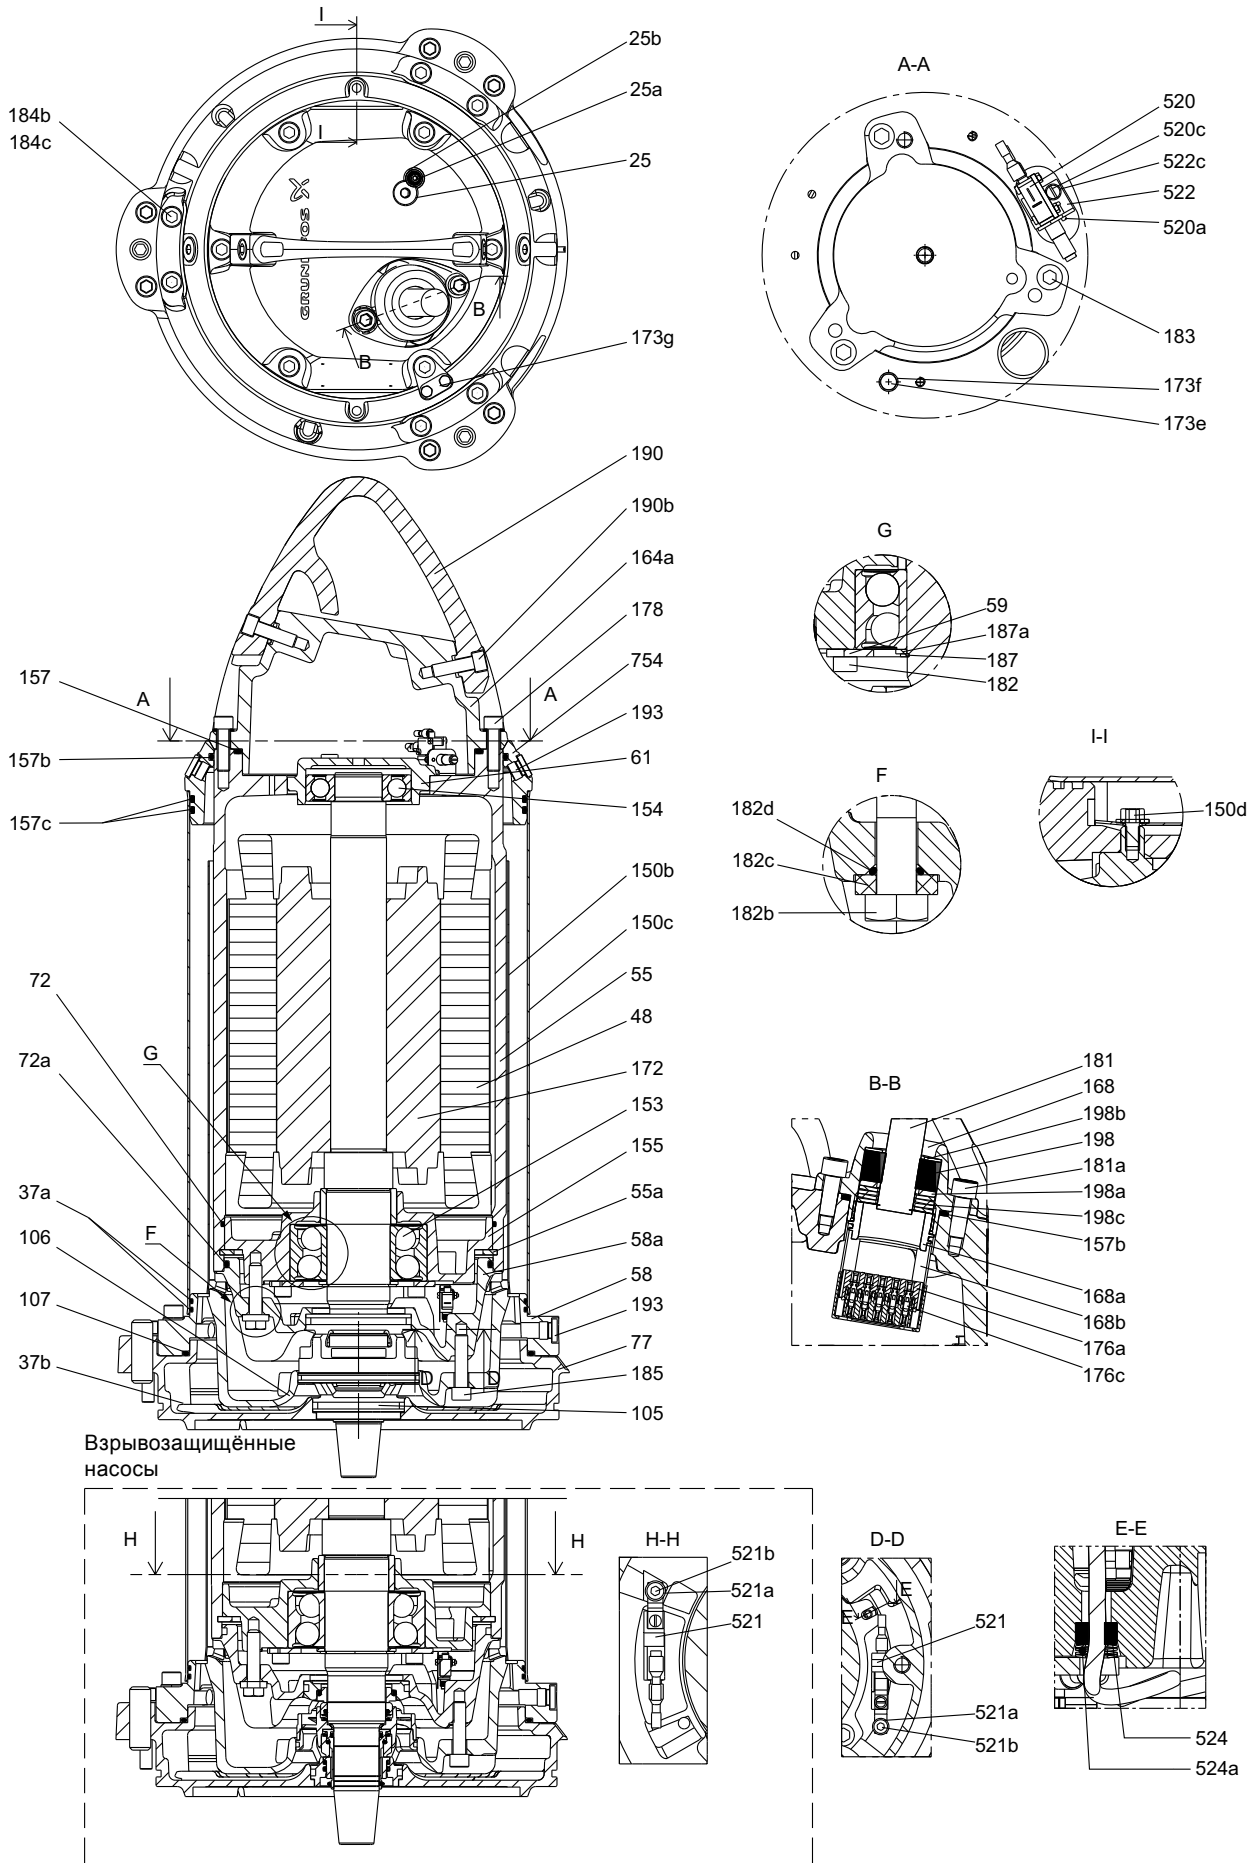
Чертеж в разрезе, насос SE с кожухом охлаждения (6-полюсные электродвигатели)
